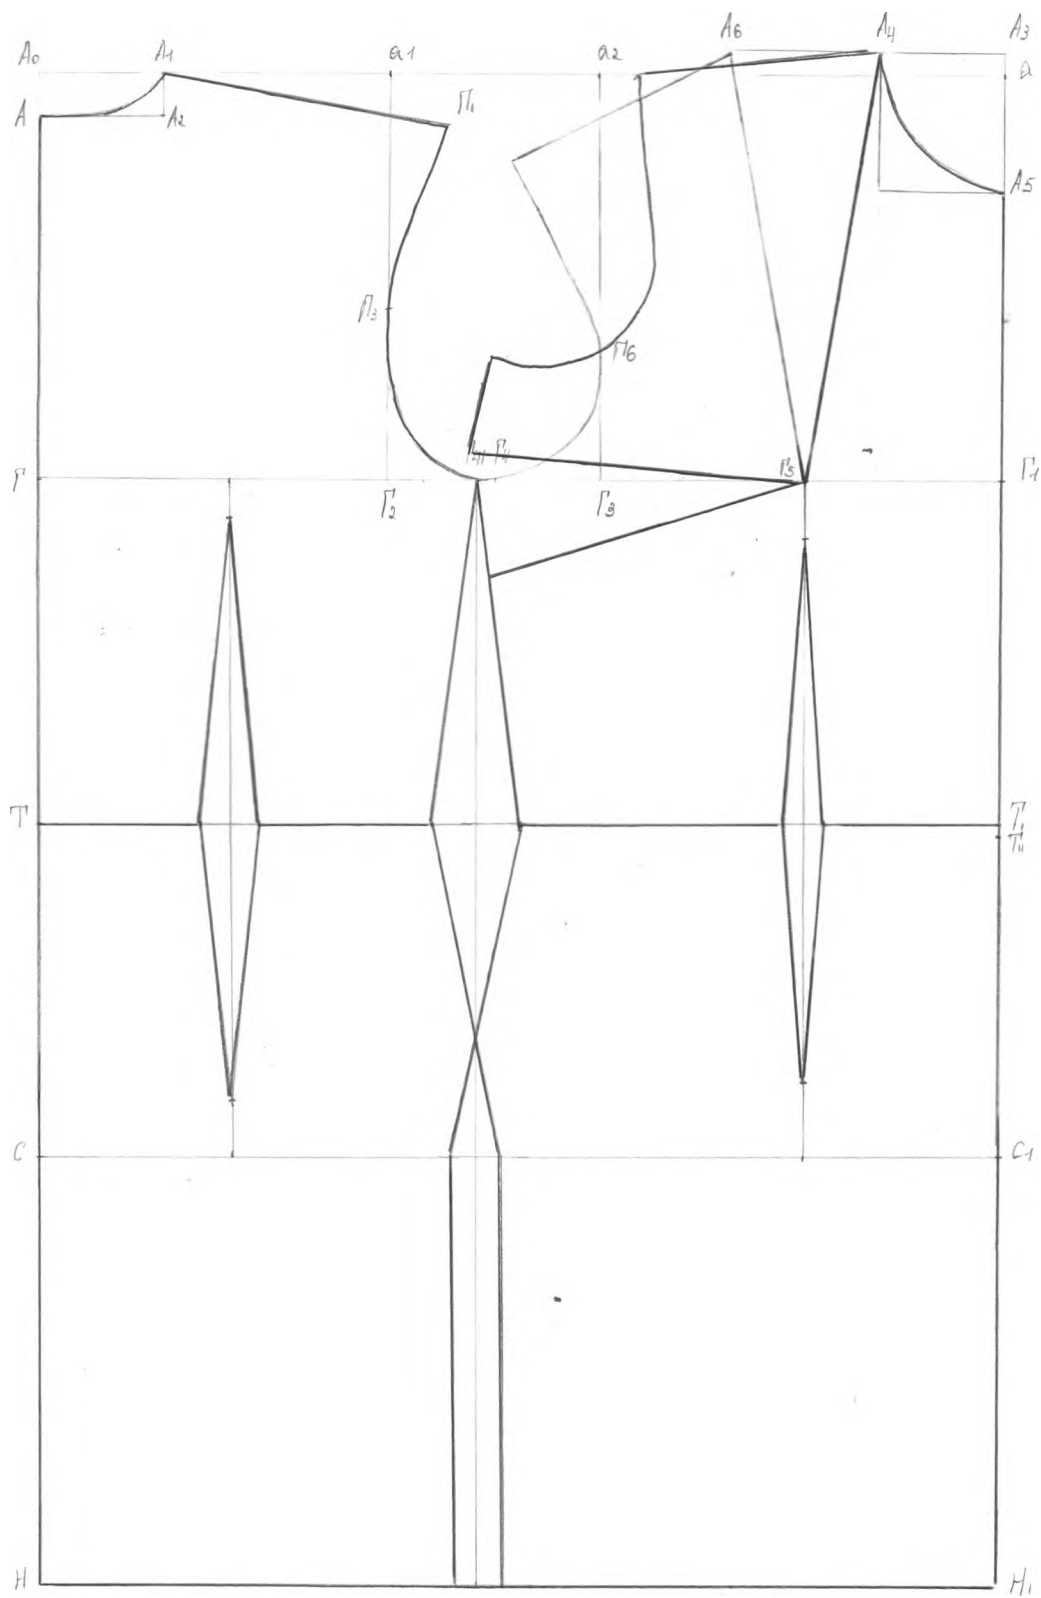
Креслення базової конструкції сукині ж'їдчої
